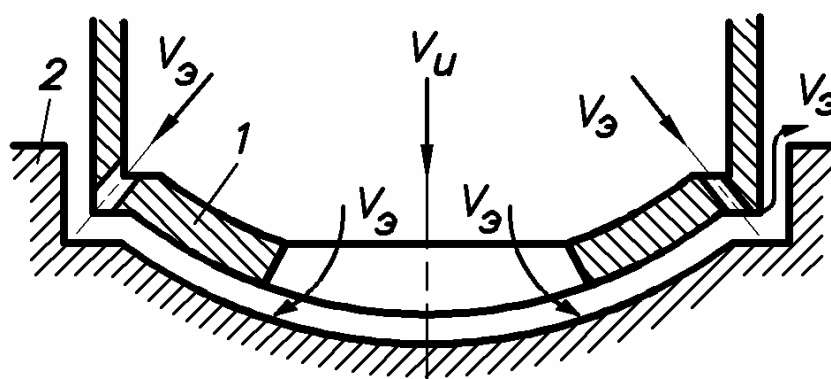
Схема обработки нескольких плавно сопряженных между собой поверхностей сложной формы:
